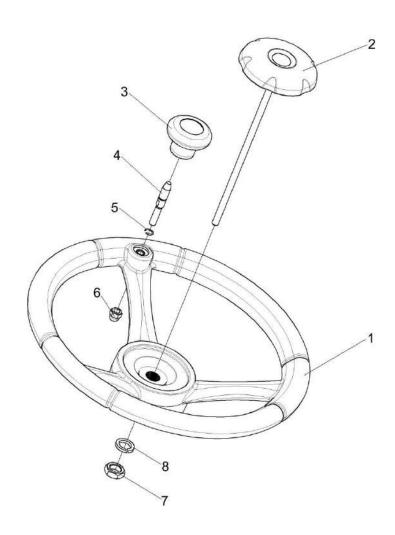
Установка колеса рулевого K3K-12-0122300 396
